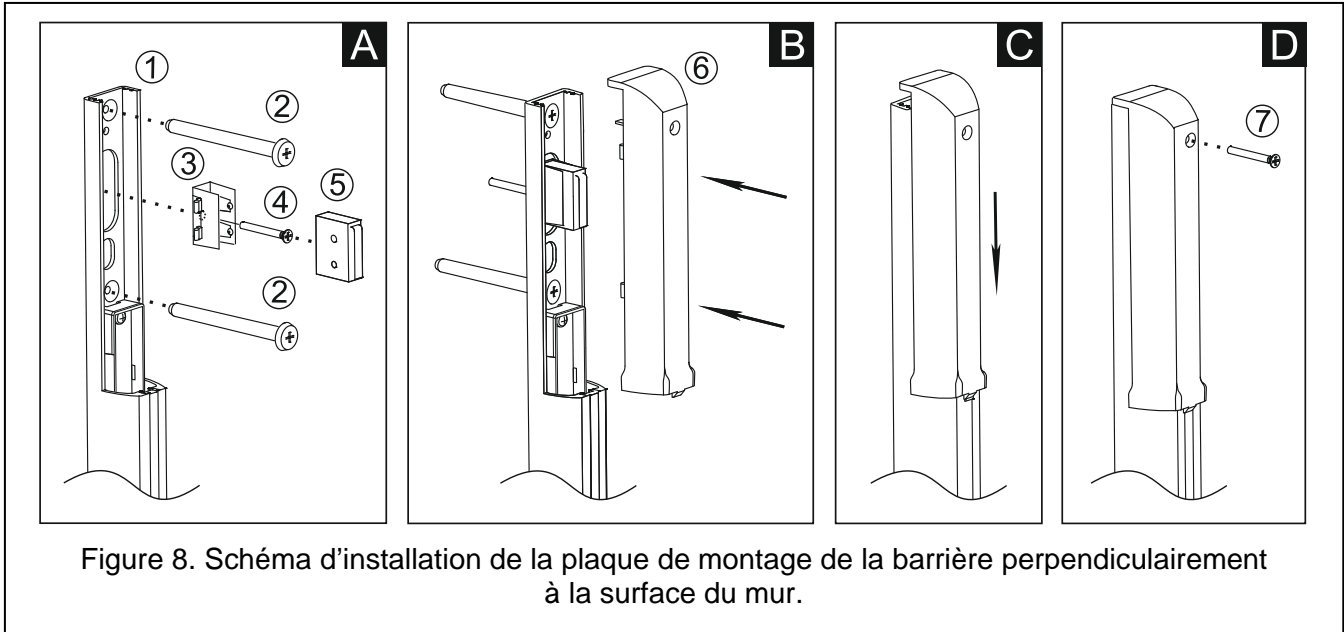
Schéma d'installation de la plaque de montage de la barrière perpendiculairement à la surface du mur.
